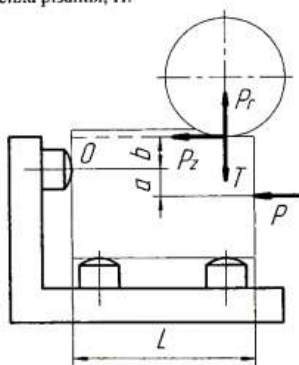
Схема для визначення сили затиску під час фрезерування
